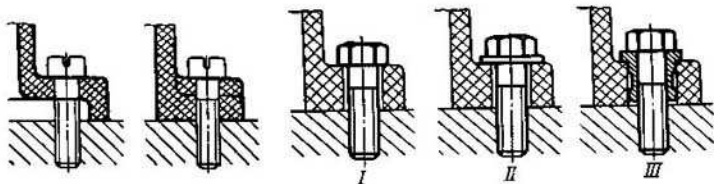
Descarga de las bridas de la flexión mediante la fuerza de apriete
